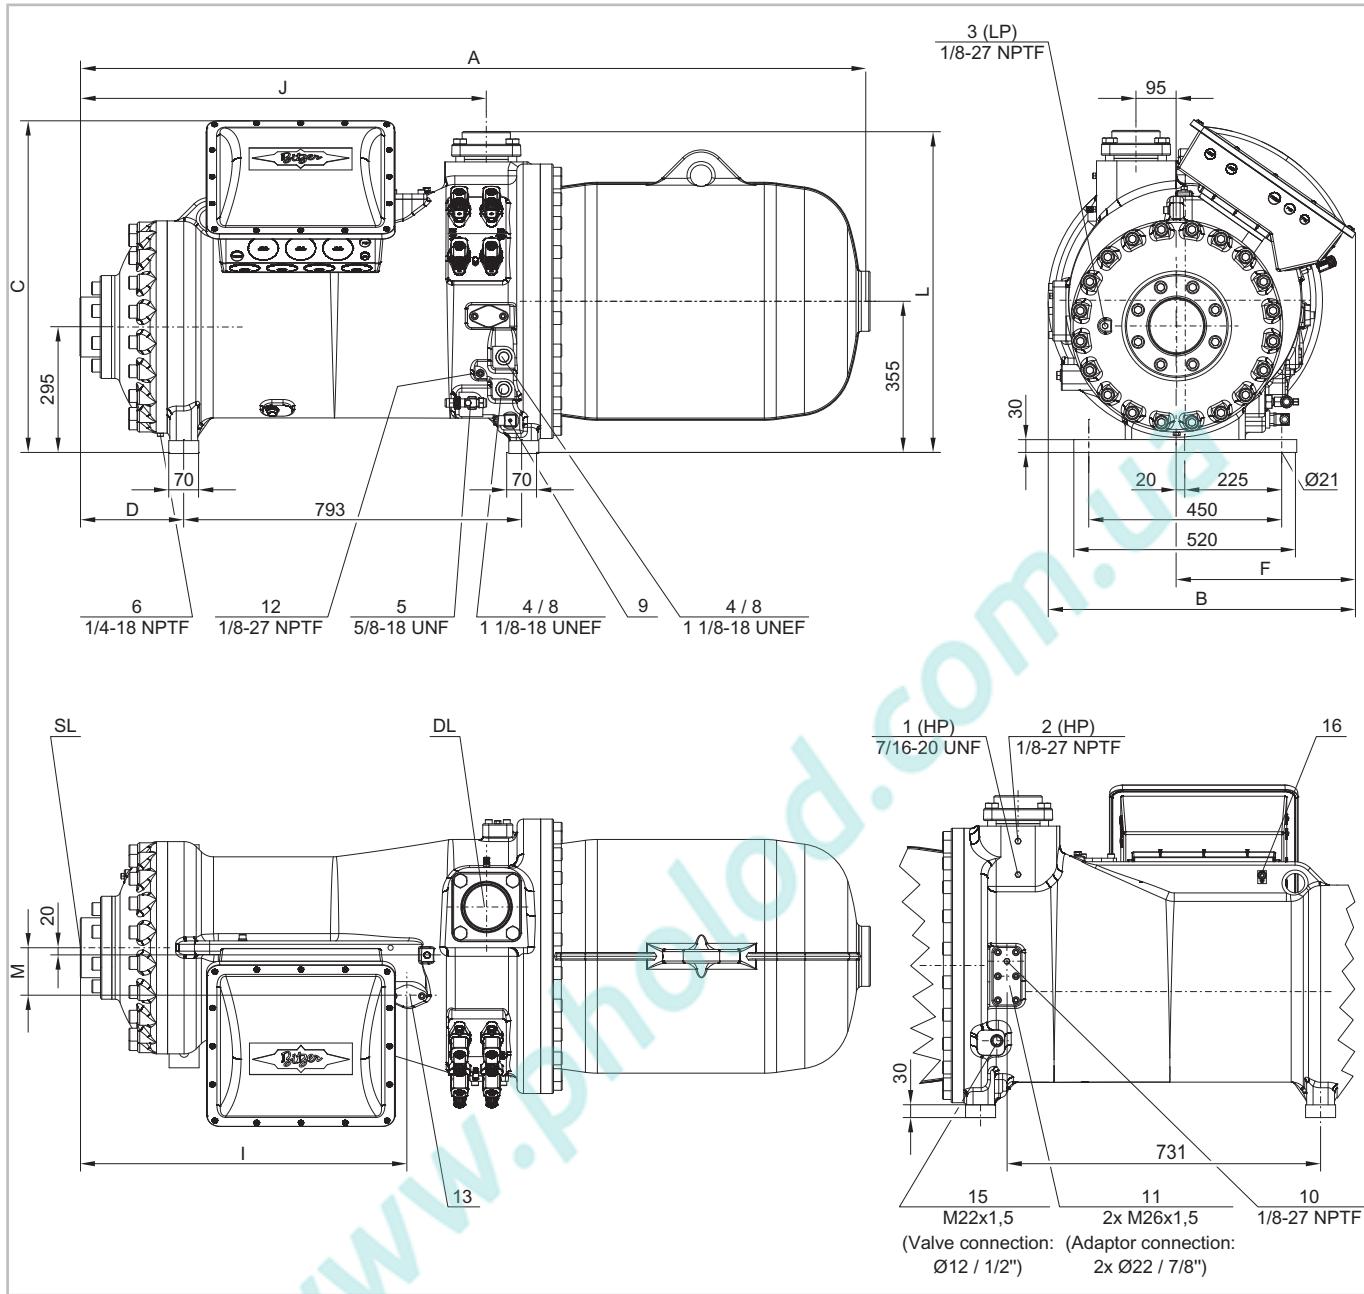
Maßzeichnung CSH9553-180(Y) .. CSH95113-320Y
